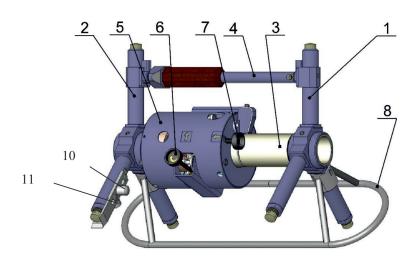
Мост оптический поворотный для дизеля 1А5Д49: 1 — крестовина правая; 2 — крестовина левая; 3 — основание; 4 — штанга; 5 — корпус оптического блока; 6 — ручка поперечного перемещения лазерного пучка; 7 — ручка продольного перемещения лазерного пучка; 8 — ограждающая рамка; 9 — фиксатор положения крестовины; 10, 11 — упор; 12 — пентапризма
